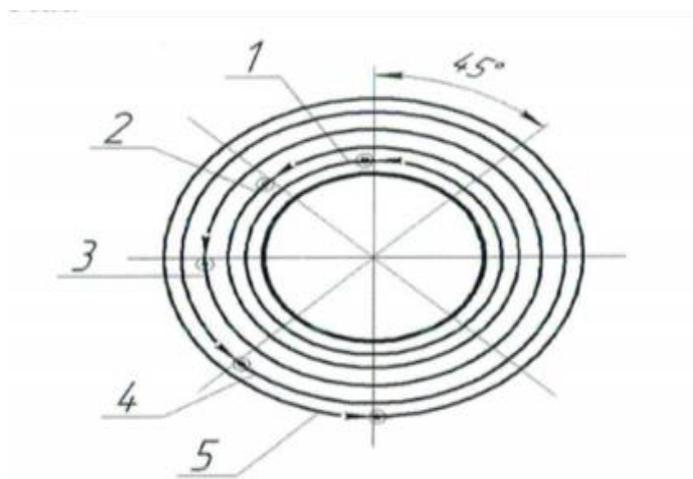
сварной стык; показан порядо наложения слоев при автоматической сварке
